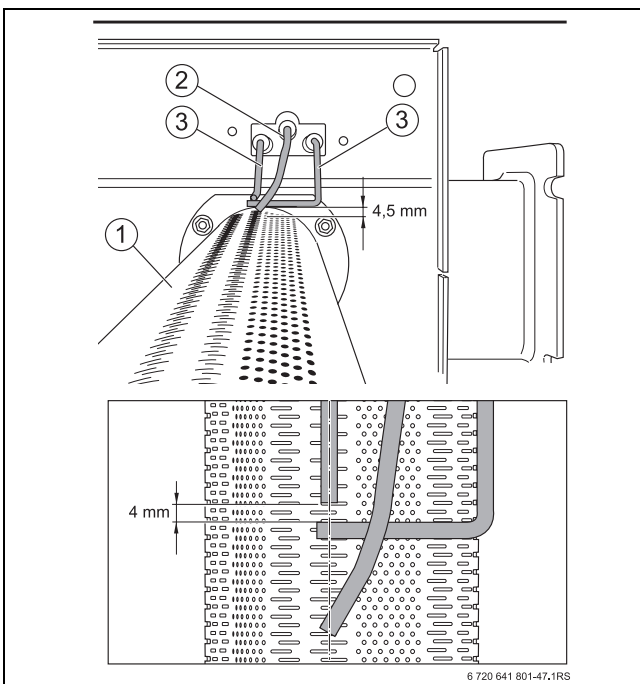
Contrôler la position des électrodes (dimensions en mm)
